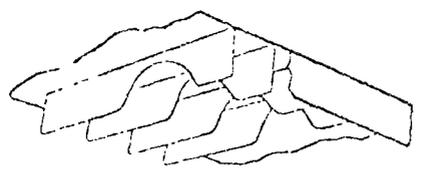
Estructura del tipo cerrado para montaje en grupo con las partes.
